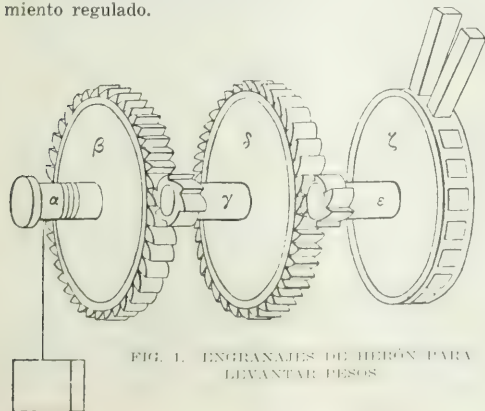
ENGRANAJES DE HERÓN PARA LEVANTAR PESOS
